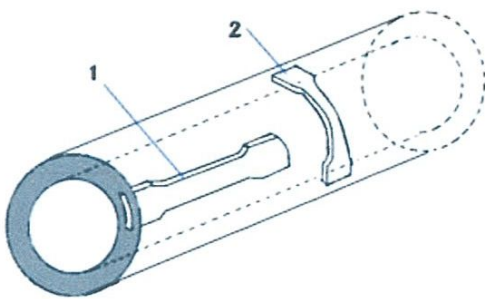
Direction de découpage des éprouvettes Figure 3-2: Dimensions des rouvettes de caractérisation
